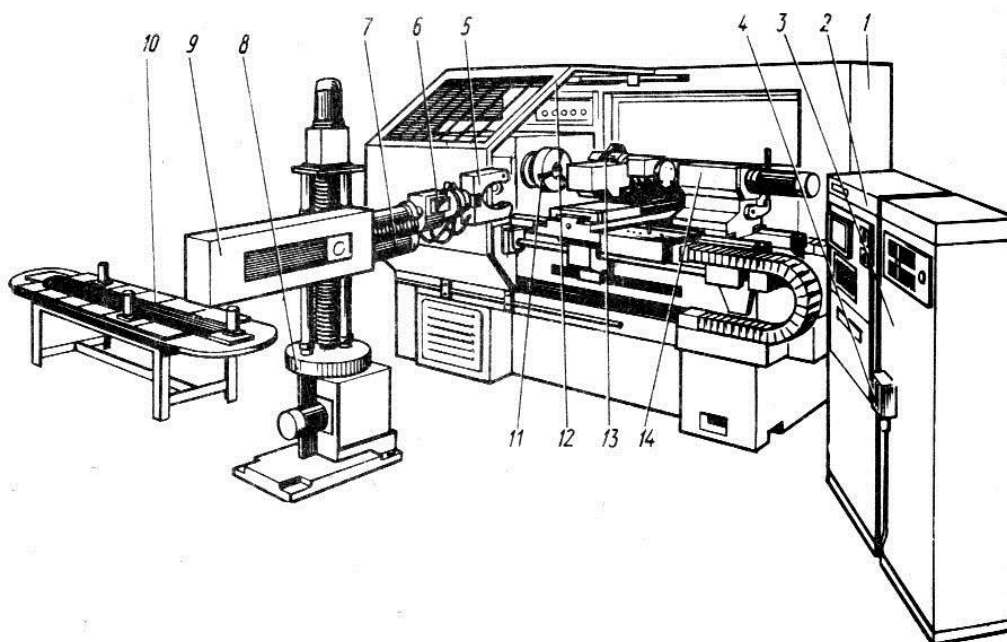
РТК на базі токарного верстата та тактового стола
